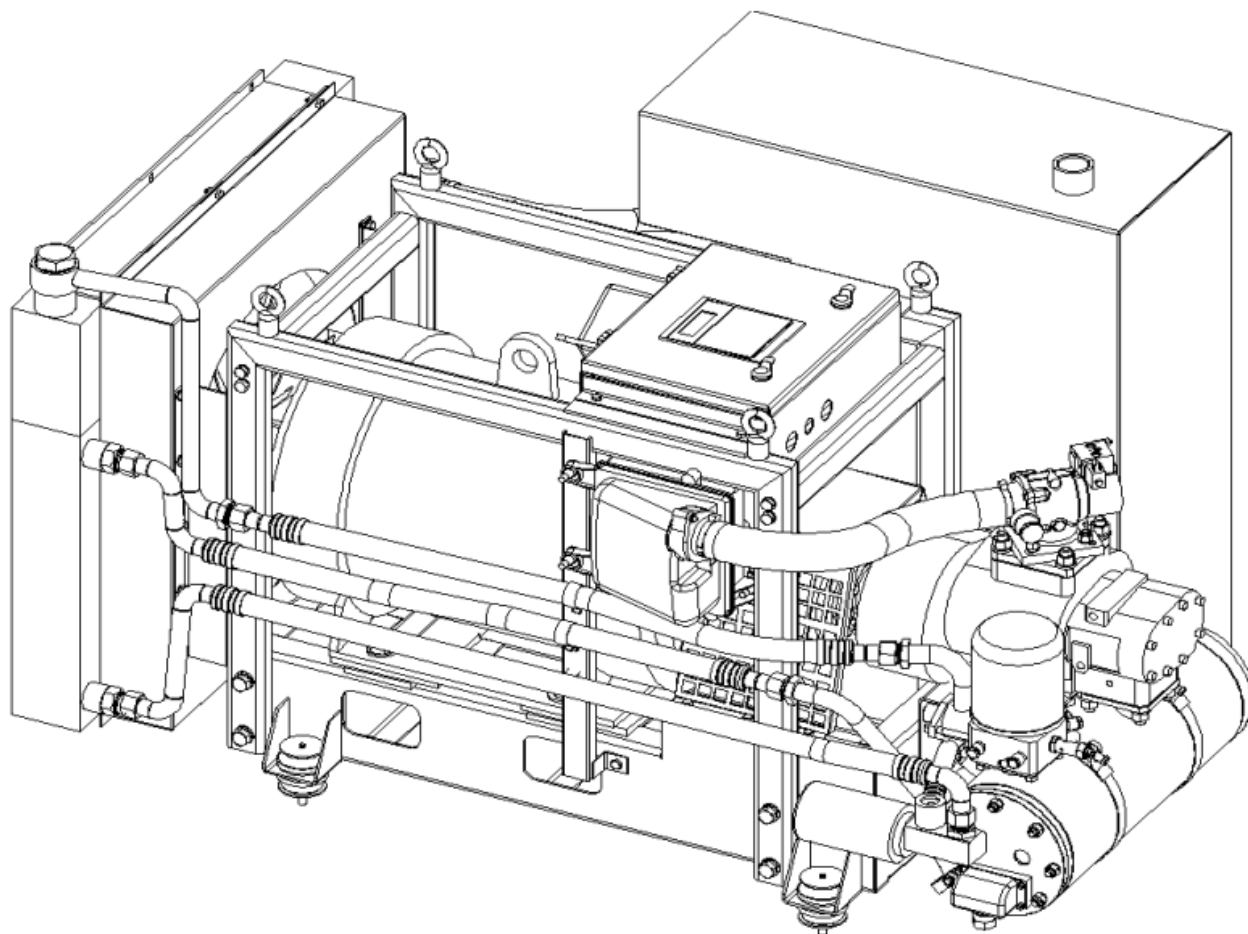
Схема компрессорного агрегата ВВ-3,5/10
